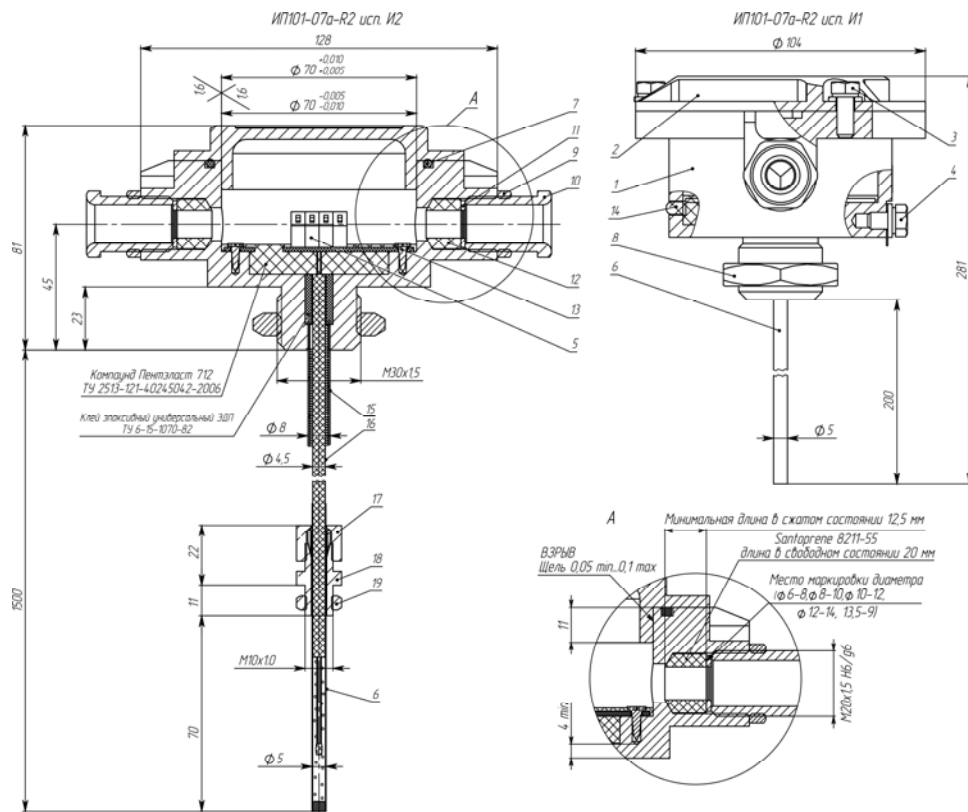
Габаритные размеры извещателя ИП101-07а-R2
